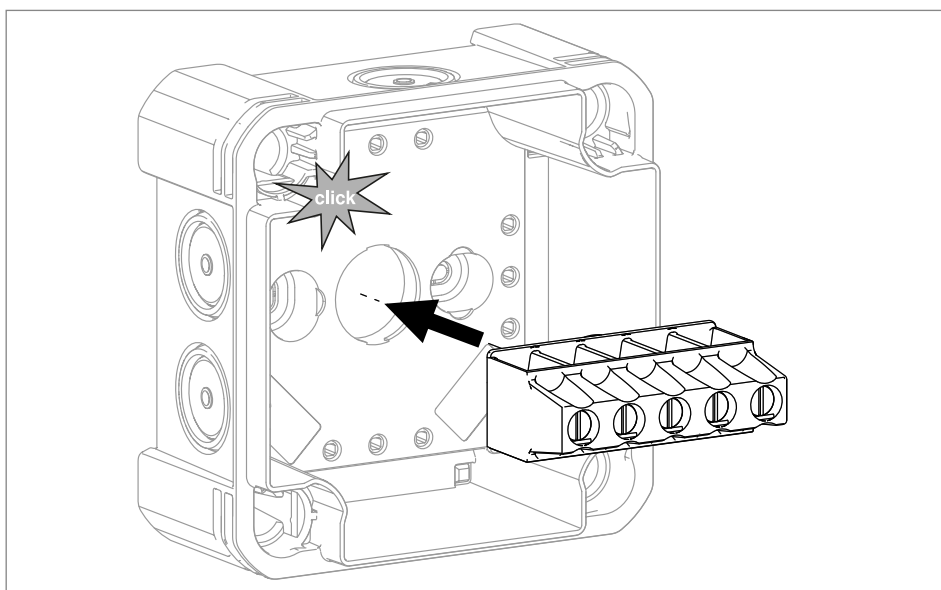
Installation d'un bornier de raccordement de type KL-T 02 06 dans la boîte de dérivation
